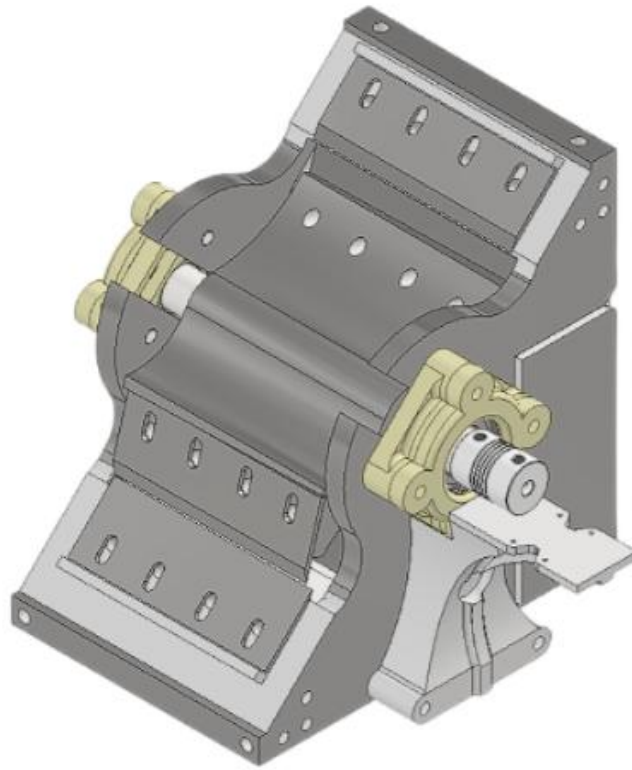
Cámaras de corte abierta prototipo 3D.
